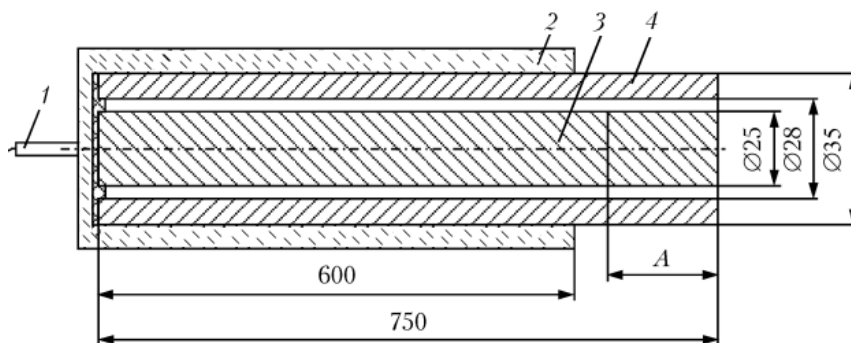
Схема зборки з дослідження каналного ефекту: 1 – детонатор; 2 – заряд ВР (амоніт 6ЖВ + аміачна селітра); 3 – сталевий циліндр; 4 – сталева оболонка, яка плакується; А – вимірювальна ділянка
